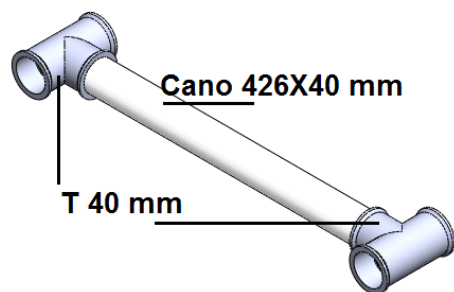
Montagem dos módulos – Módulo 4 – Passo 1
